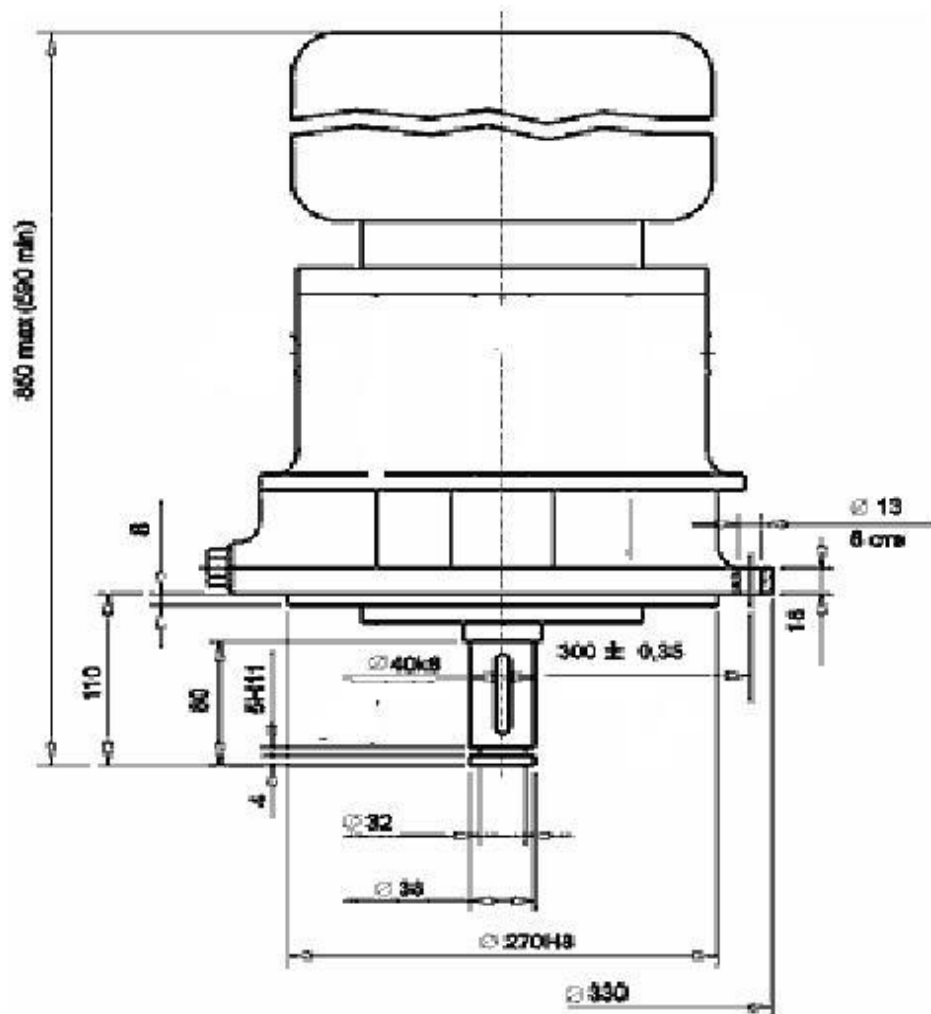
Зовнішній вигляд і габаритні розміри редуктора МПО1М
